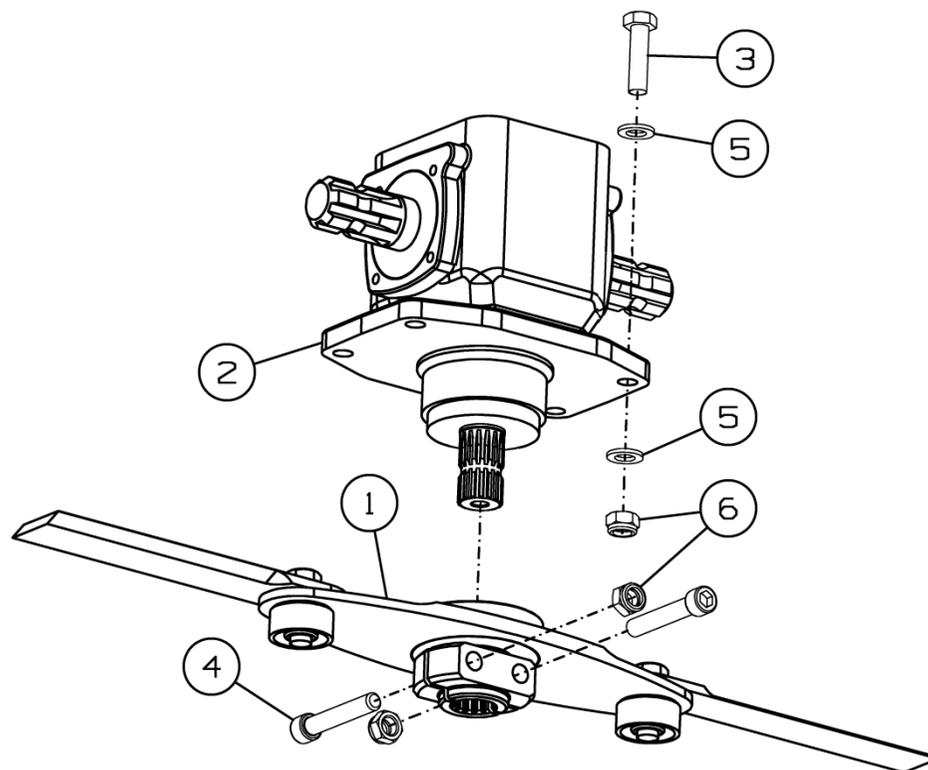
Редуктор в сборе SS-780.01.08.040
